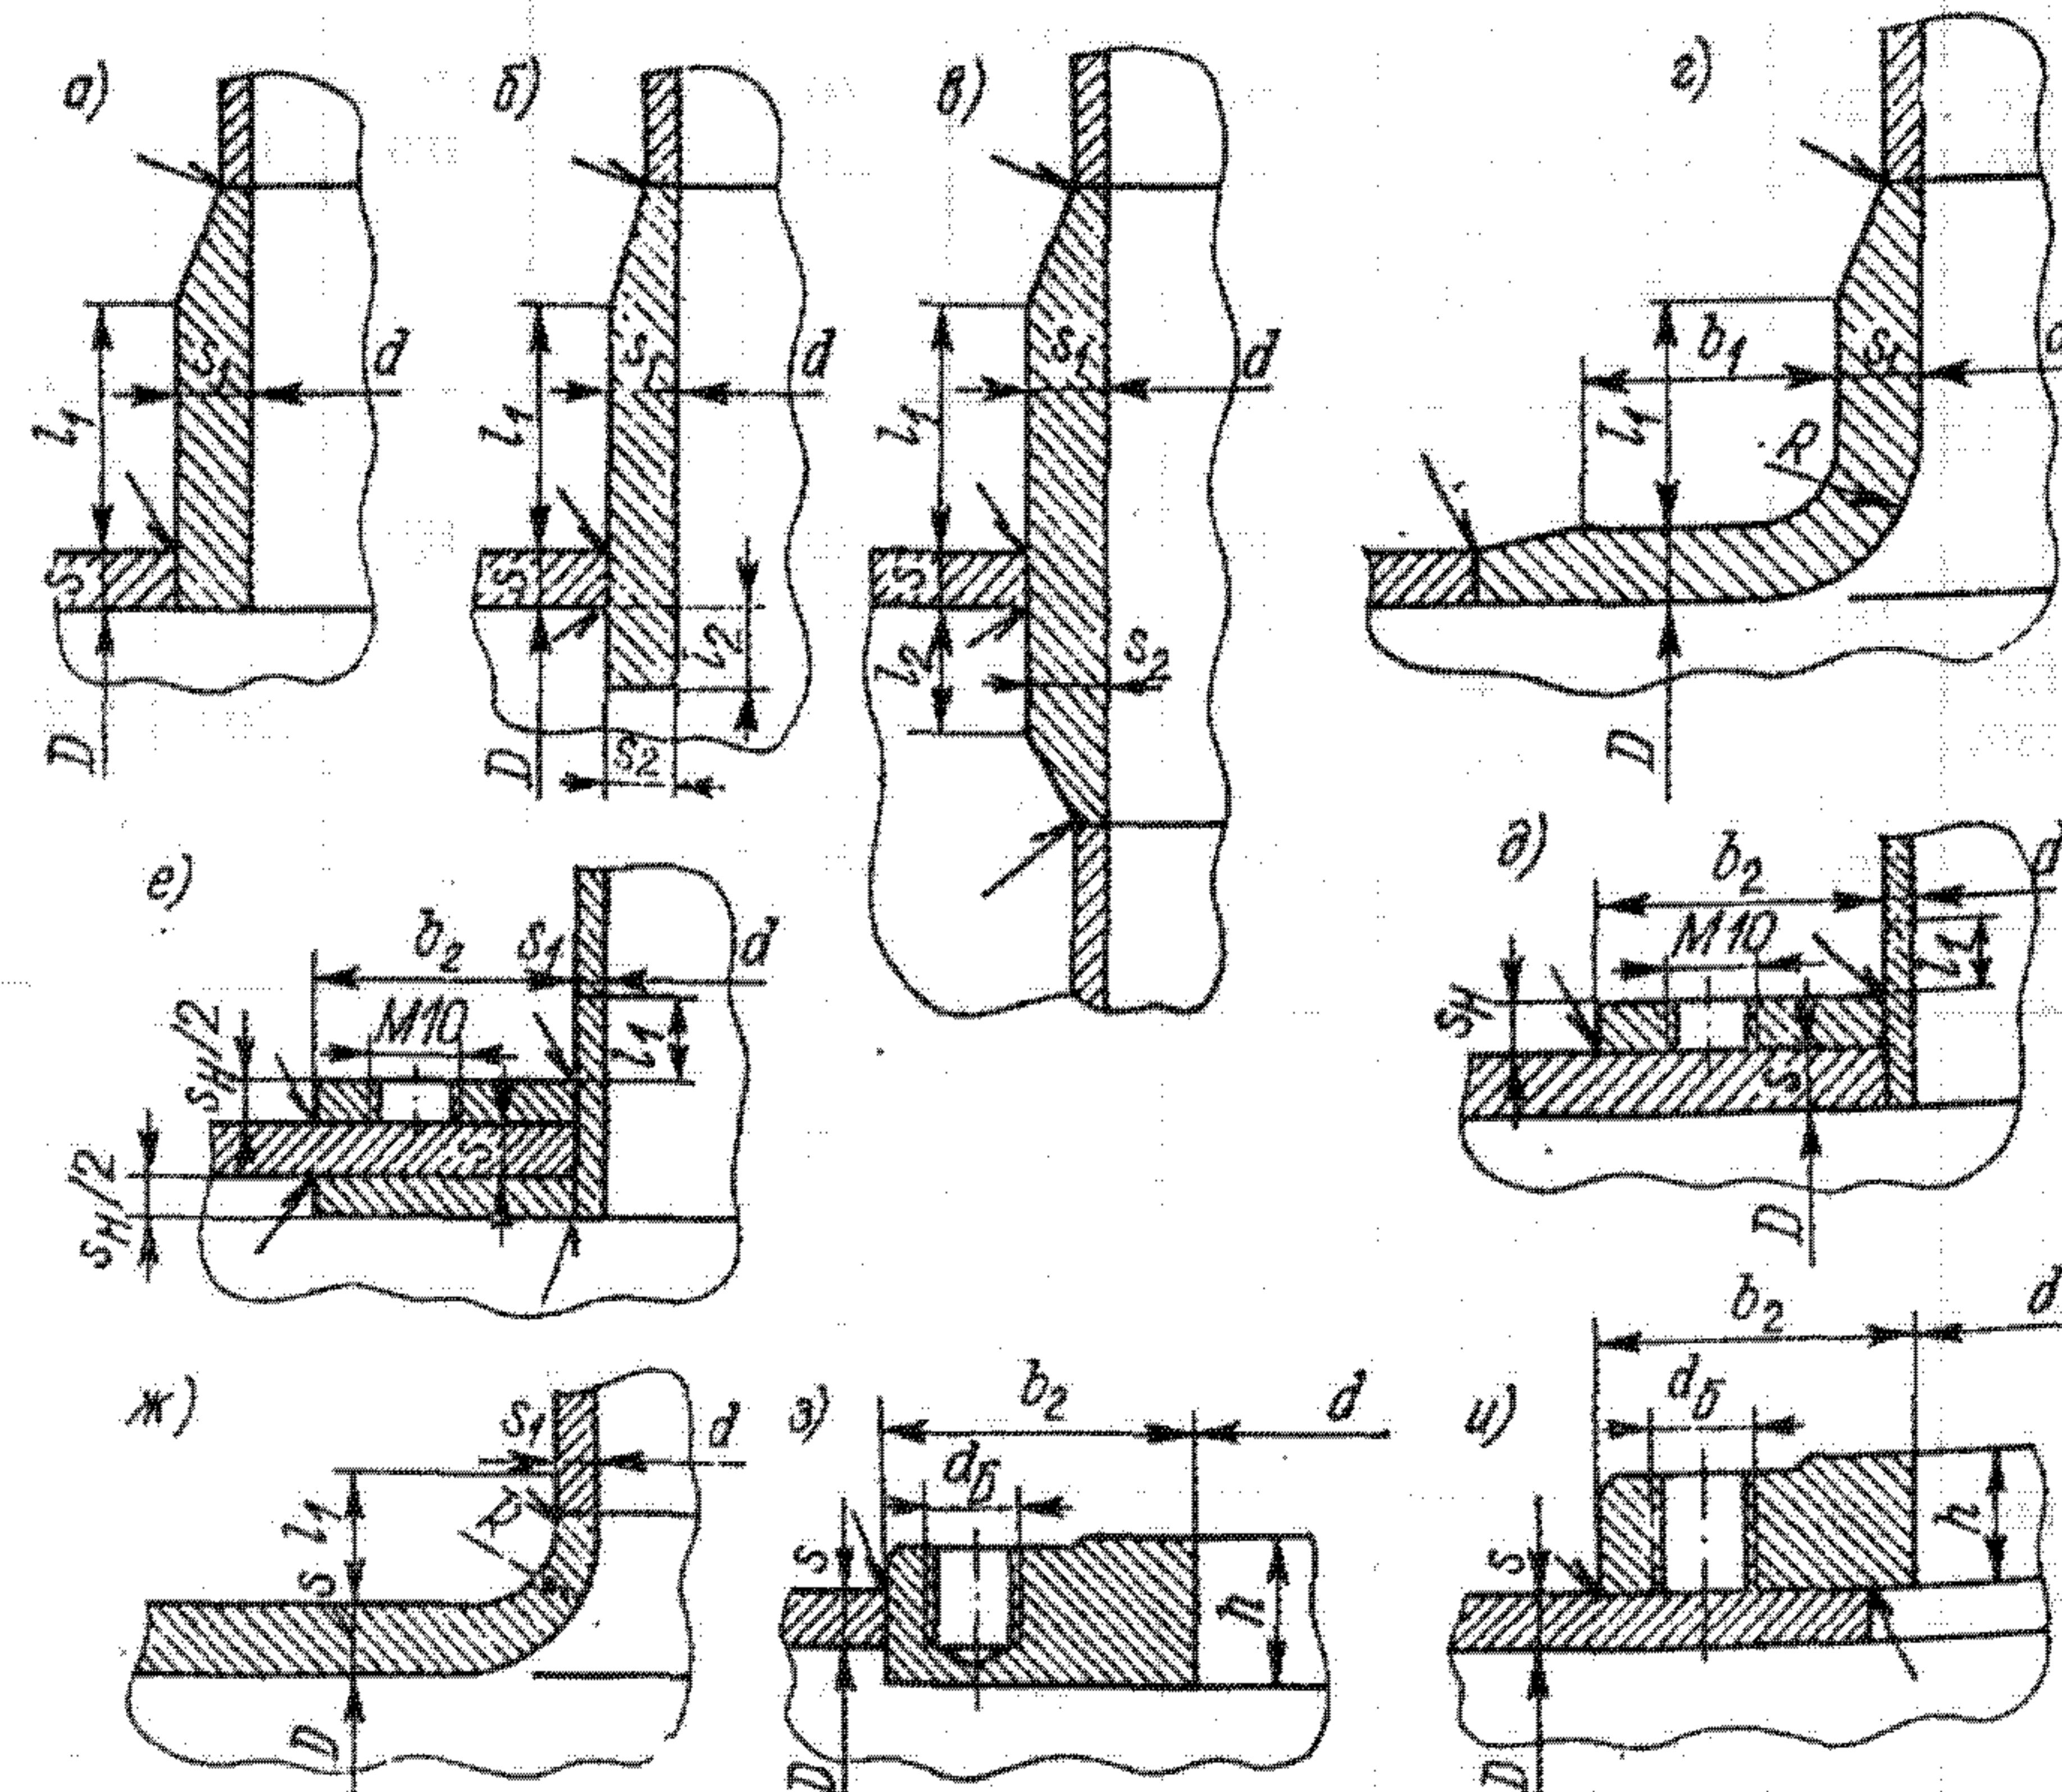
Конструкции укреплений отверстий в стенках сварных аппаратов:
